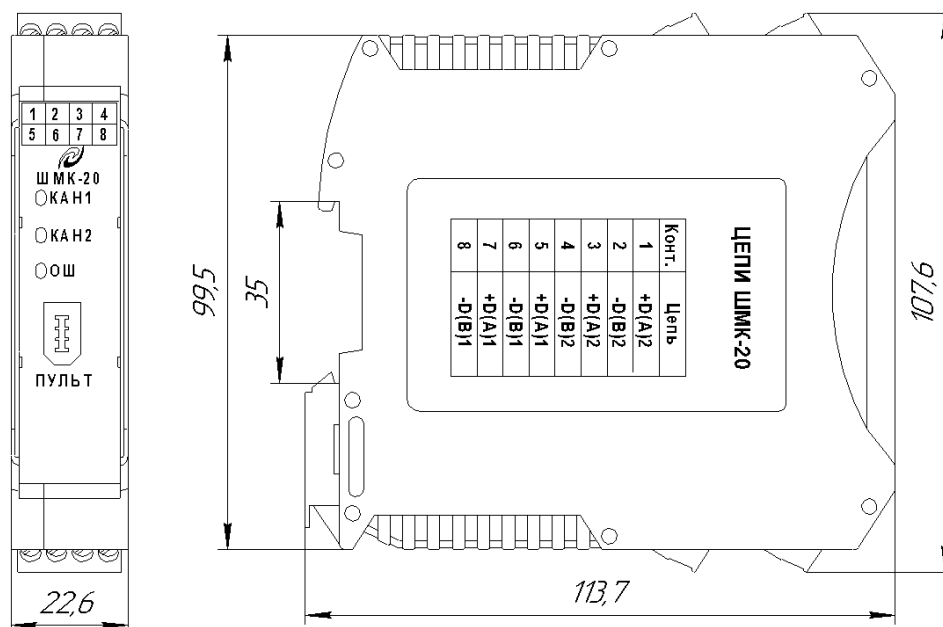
, б – Внешний вид и габаритные размеры микроконтроллера ШМК-20
